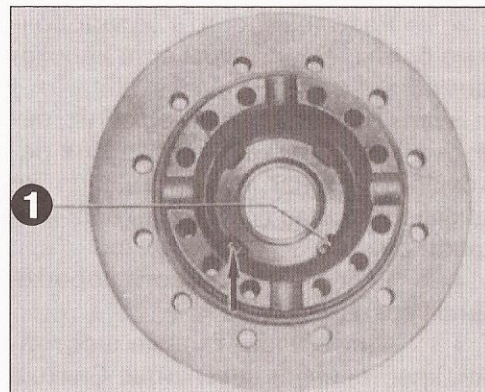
Для снятия подшипника дифференциала, расположенного со стороны ведомой шестерни, предусмотрены отверстия для установки технологического стержня.
